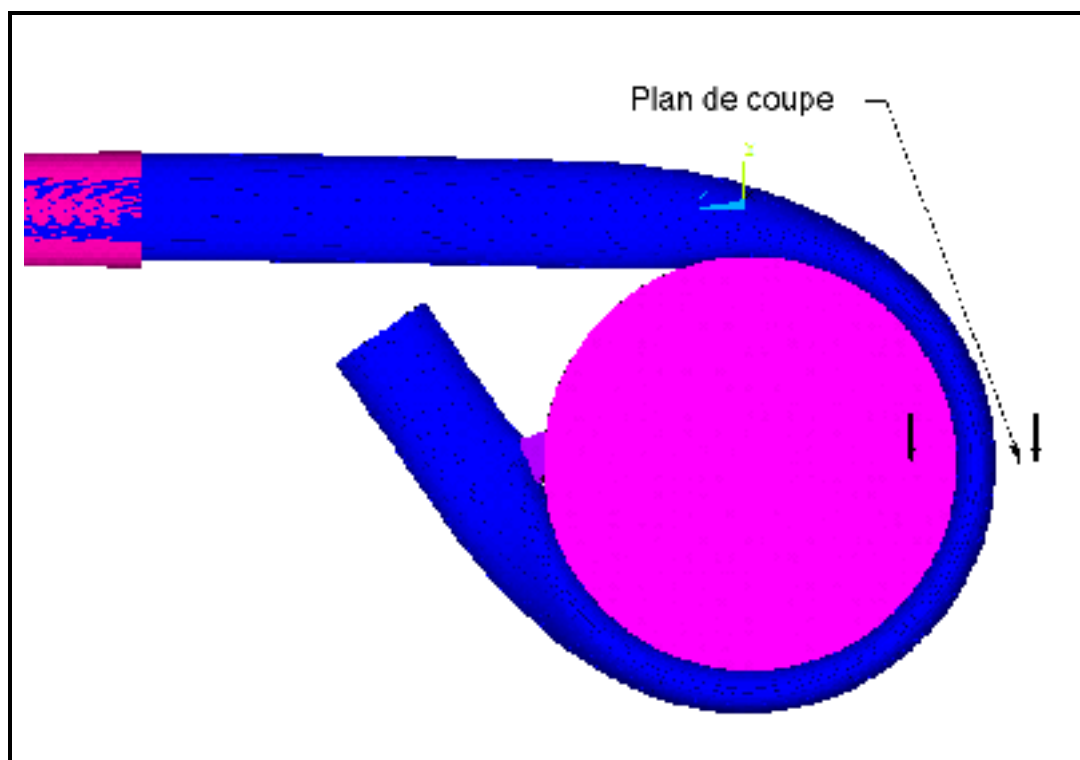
Vue de côté du modèle enroulé avec plan de coupe
